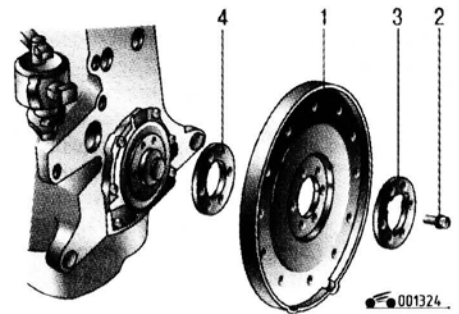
Ведущий диск: 1 – ведущий диск; 2 – болт крепления ведущего диска; 3 – прижимная пластина; 4 – регулировочная шайба
